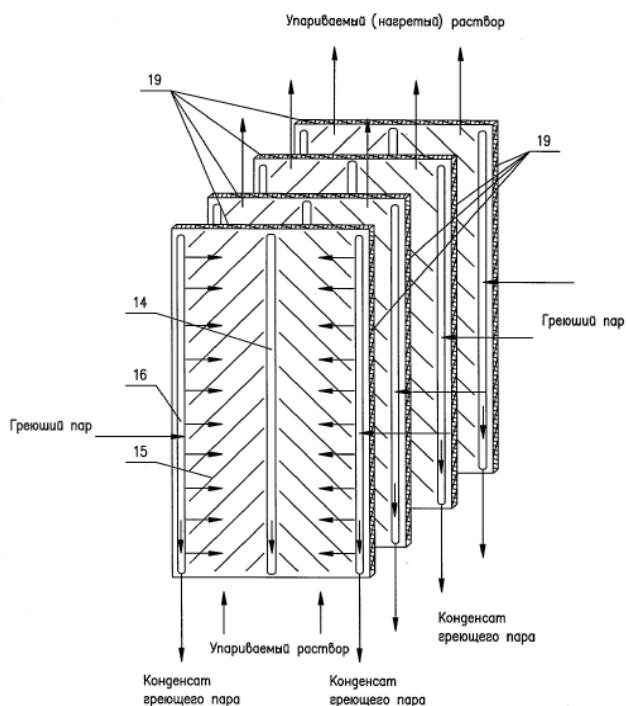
Компоновка попарно сваренных пластин разборной греющей камеры
